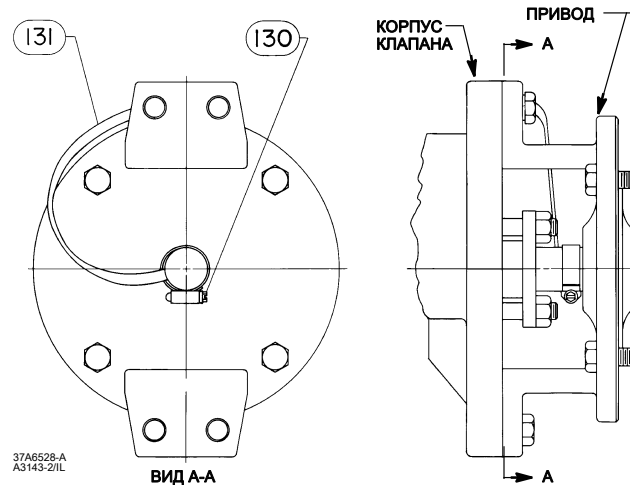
Контактная перемычка в сборе для электрической связи штока и корпуса (опция)
